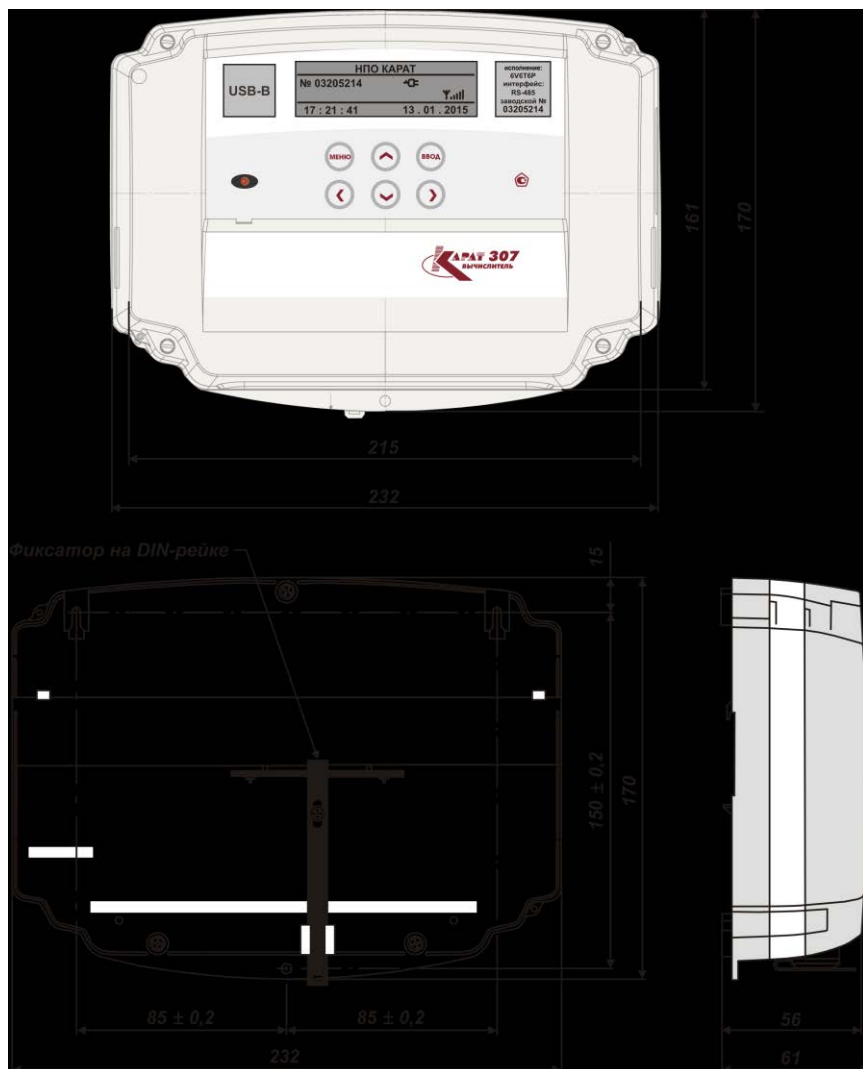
Габаритные и установочные размеры вычислителя
